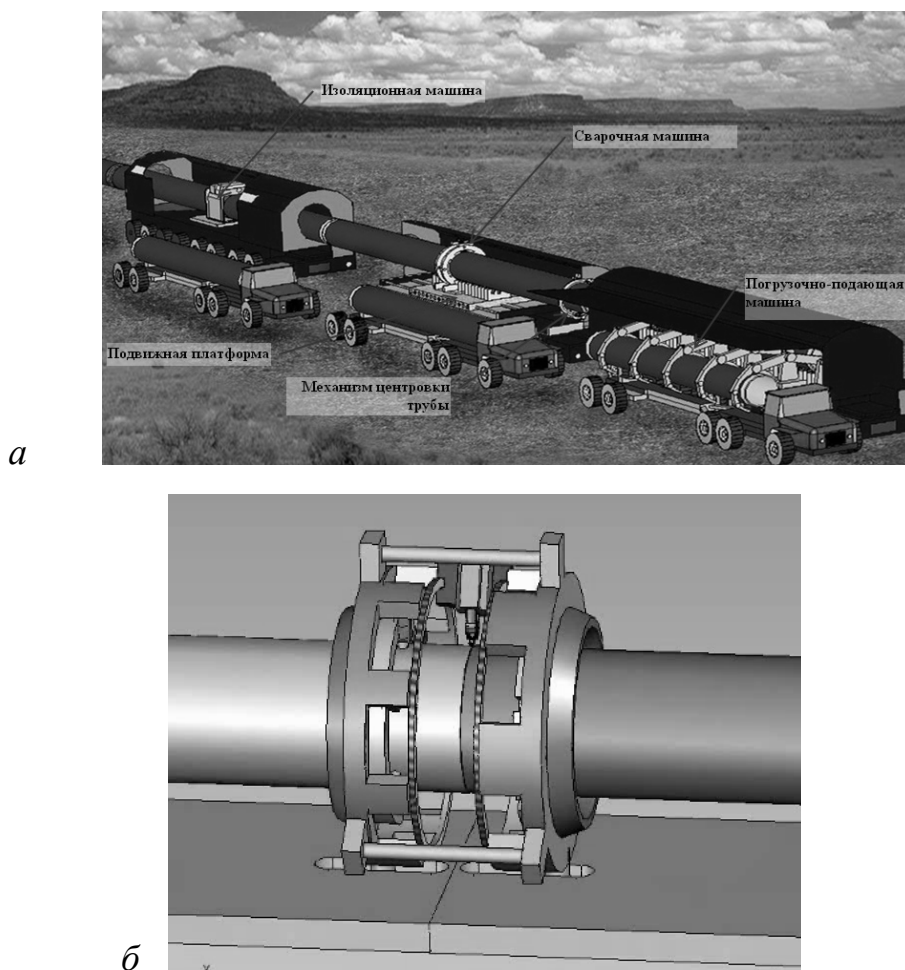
Автоматизированный мобильный комплекс (*а*) и модуль (*б*) для лазерной сварки стыков трубопроводов в полевых условиях
